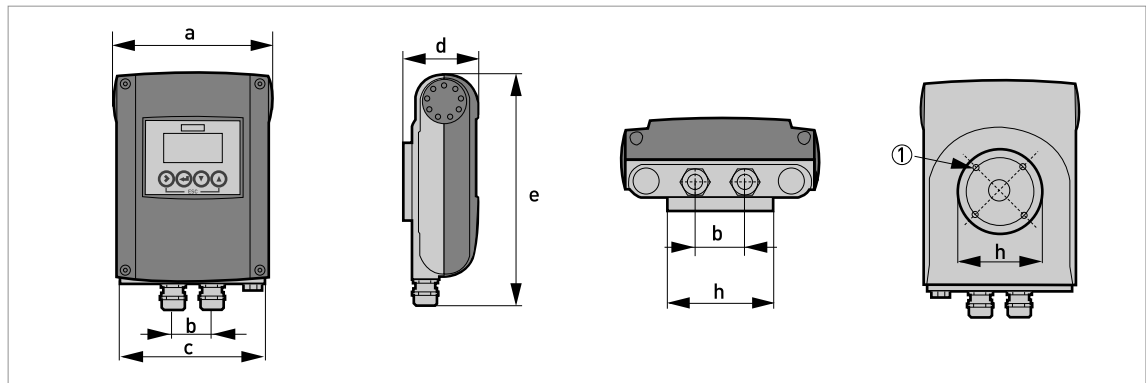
Abmessungen für Kompaktausführung (0°), Aluminiumgehäuse
